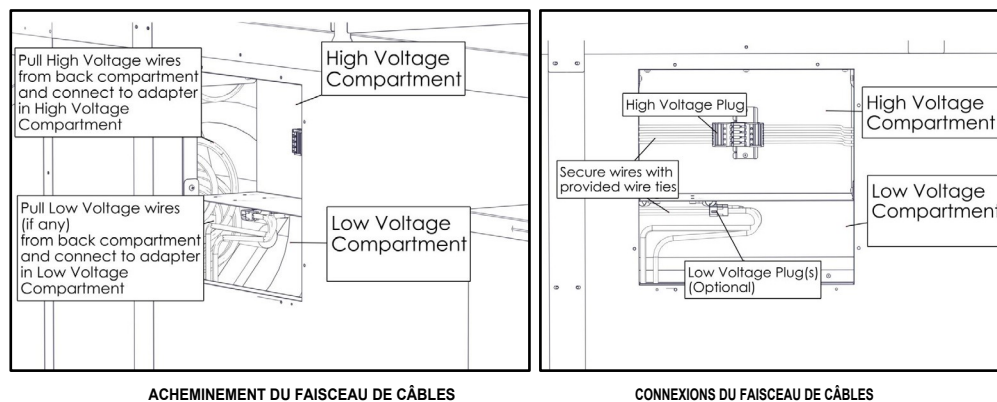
DÉTAILS DU FAISCEAU DE CÂBLES (SUITE)
